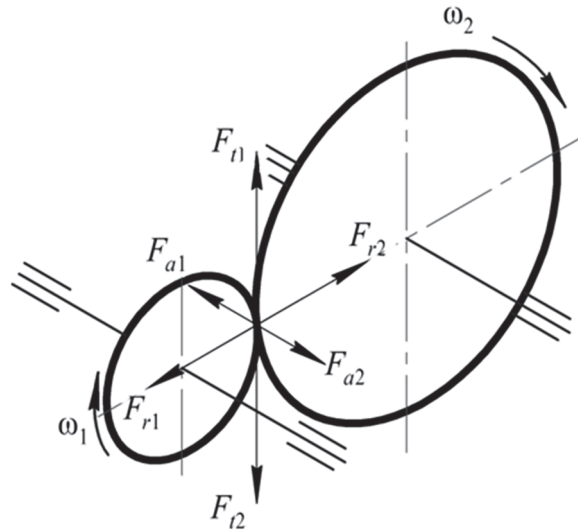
Схема сил в цилиндрической косозубой зубчатой передаче
